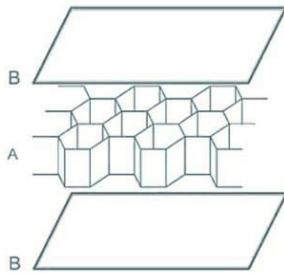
Aufbau einer Pappe mit Wabenstruktur
